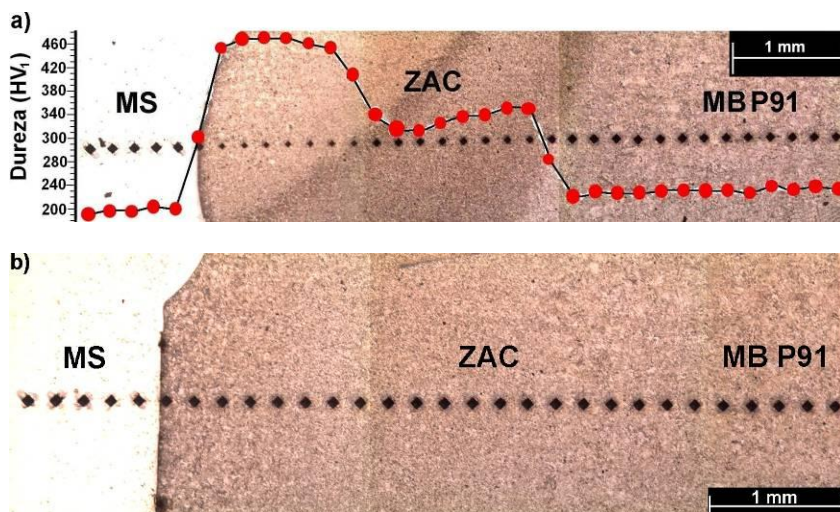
Macrografias da solda dissimilar DPI após o TT: (a) junto à superfície do tubo; (b) metade da espessura. Ataque químico: Villela.
